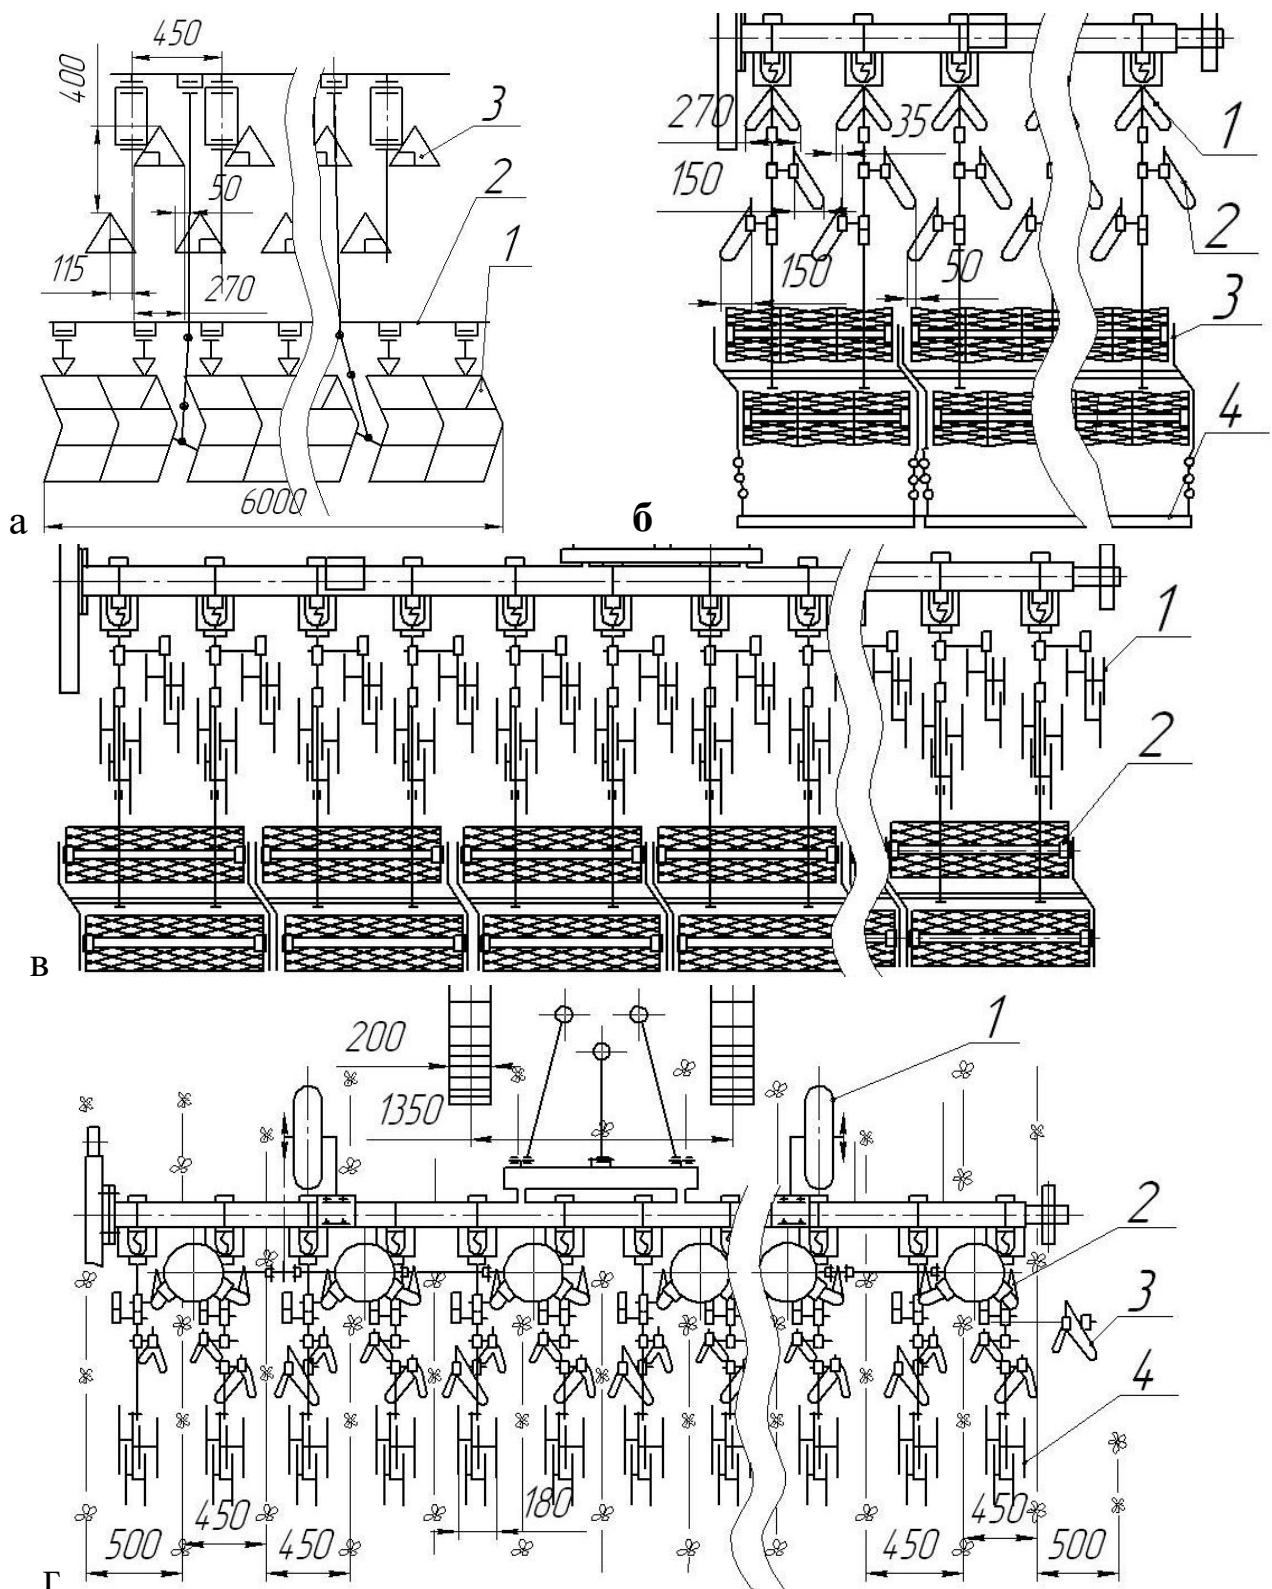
Схемы расстановки рабочих органов культиватора:
